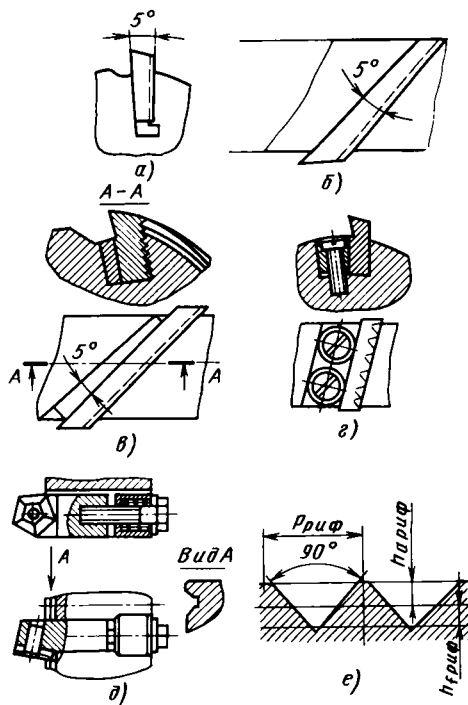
Виды крепления режущих элементов сборных инструментов
